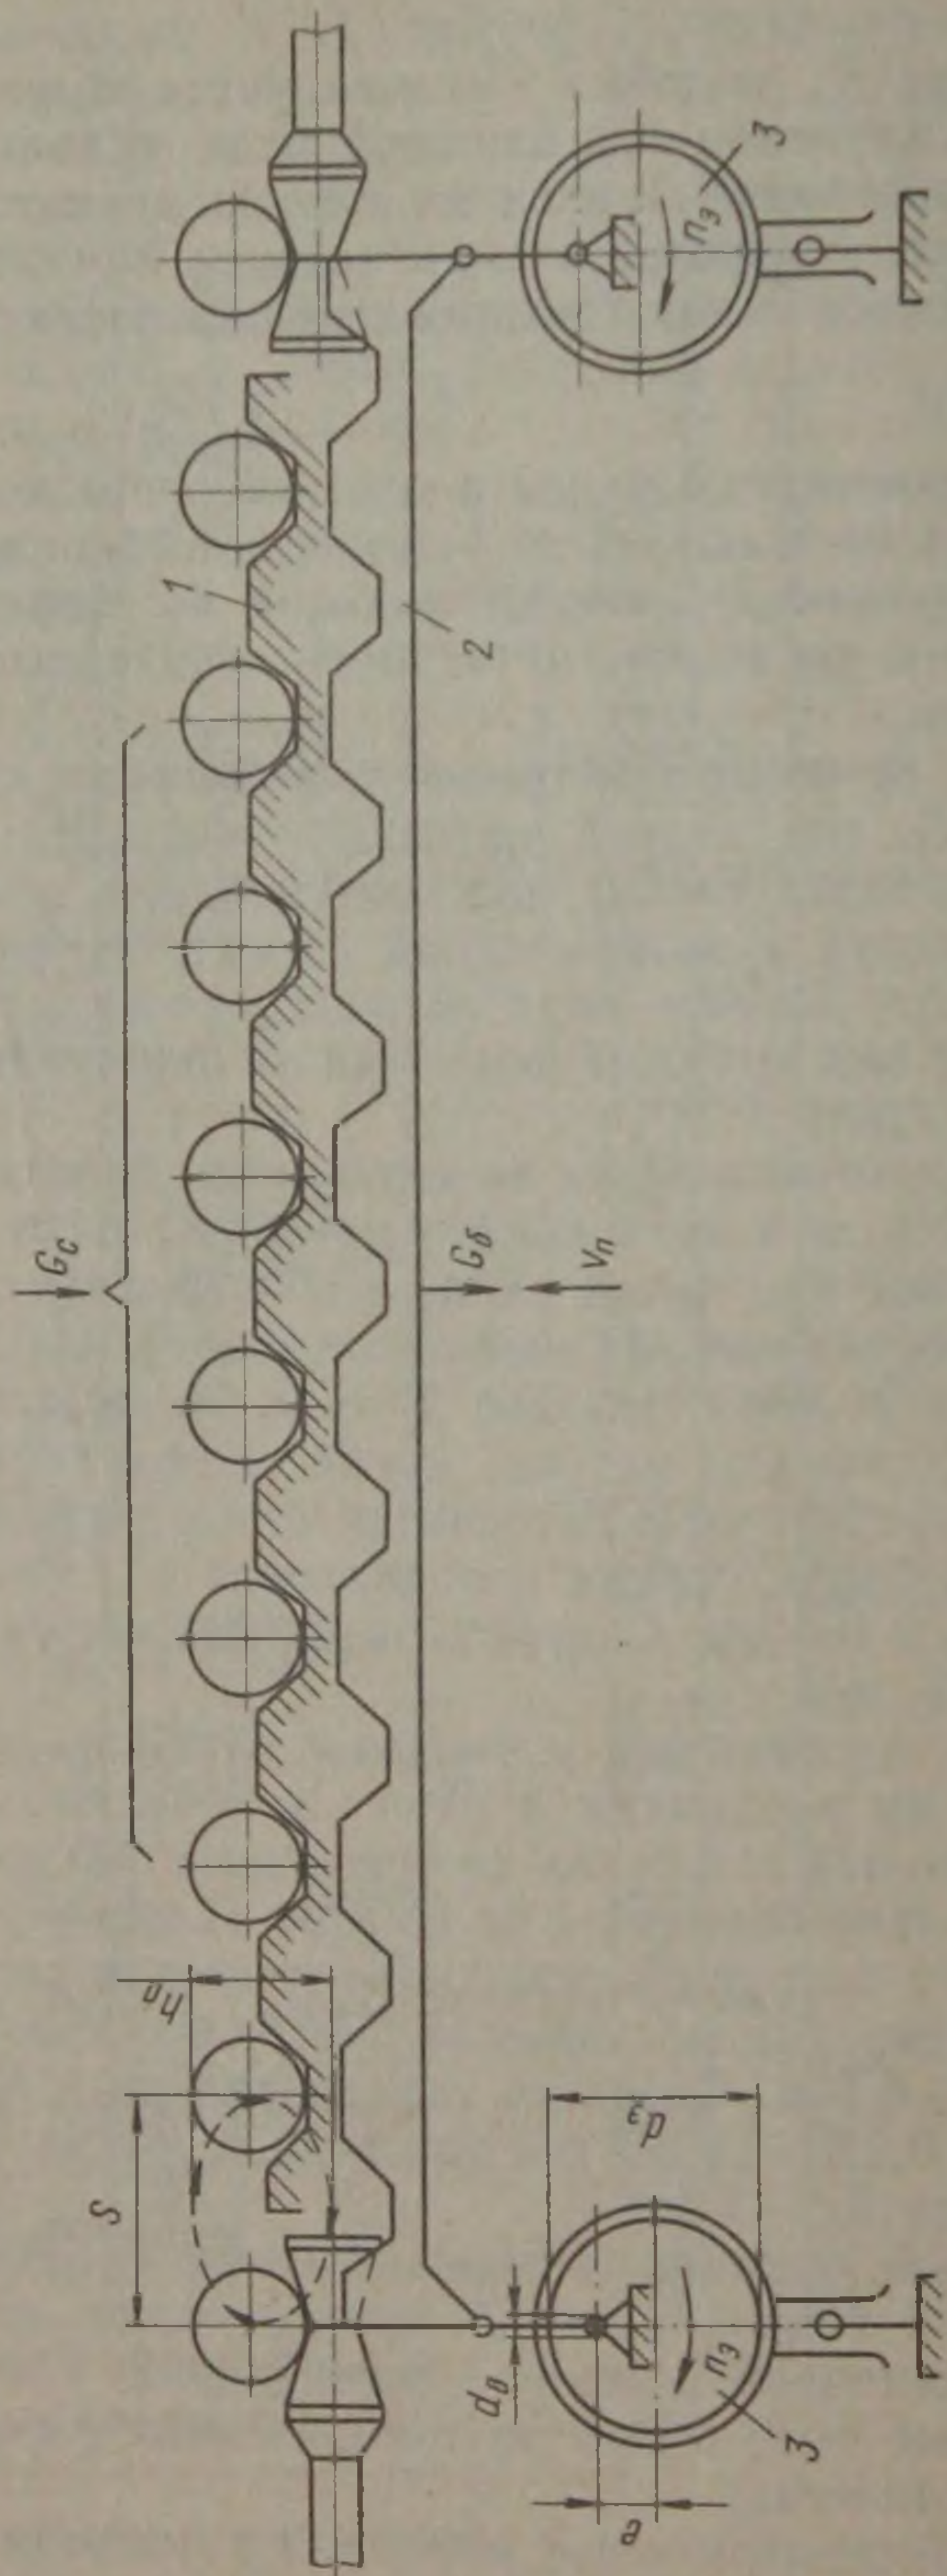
Печной шагающий конвейер для заготовок круглого сечения
